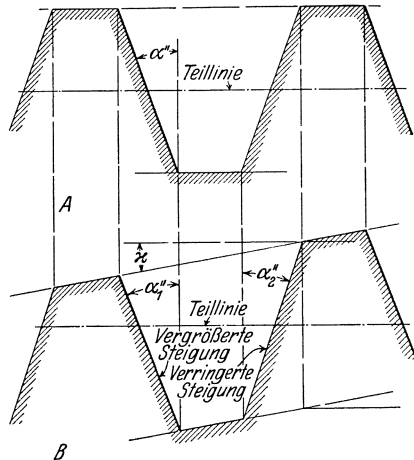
A Axialschnitt einer Frässhnecke, B Axialschnitt eines hinterarbeiteten Abwälzfräsers.
